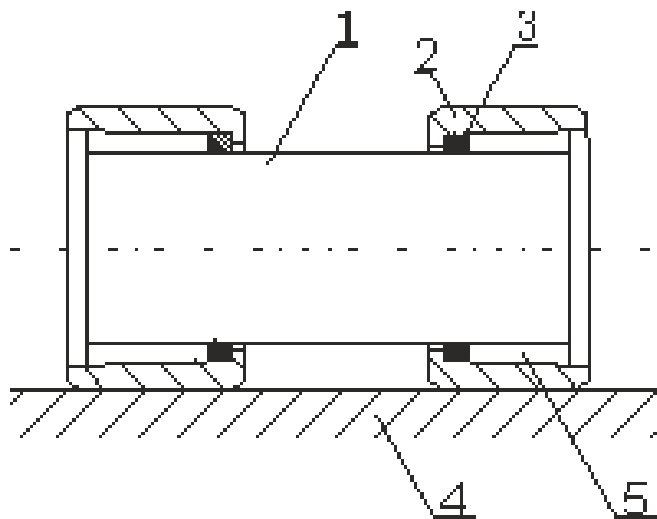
Схема центрирования и закрепления образца в обоймах устройства
